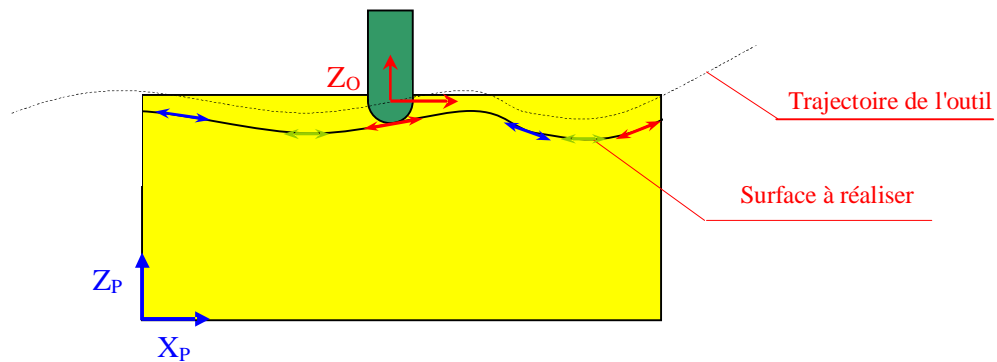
Trajectoire de l'outil dans un plan parallèle au plan XZ.
